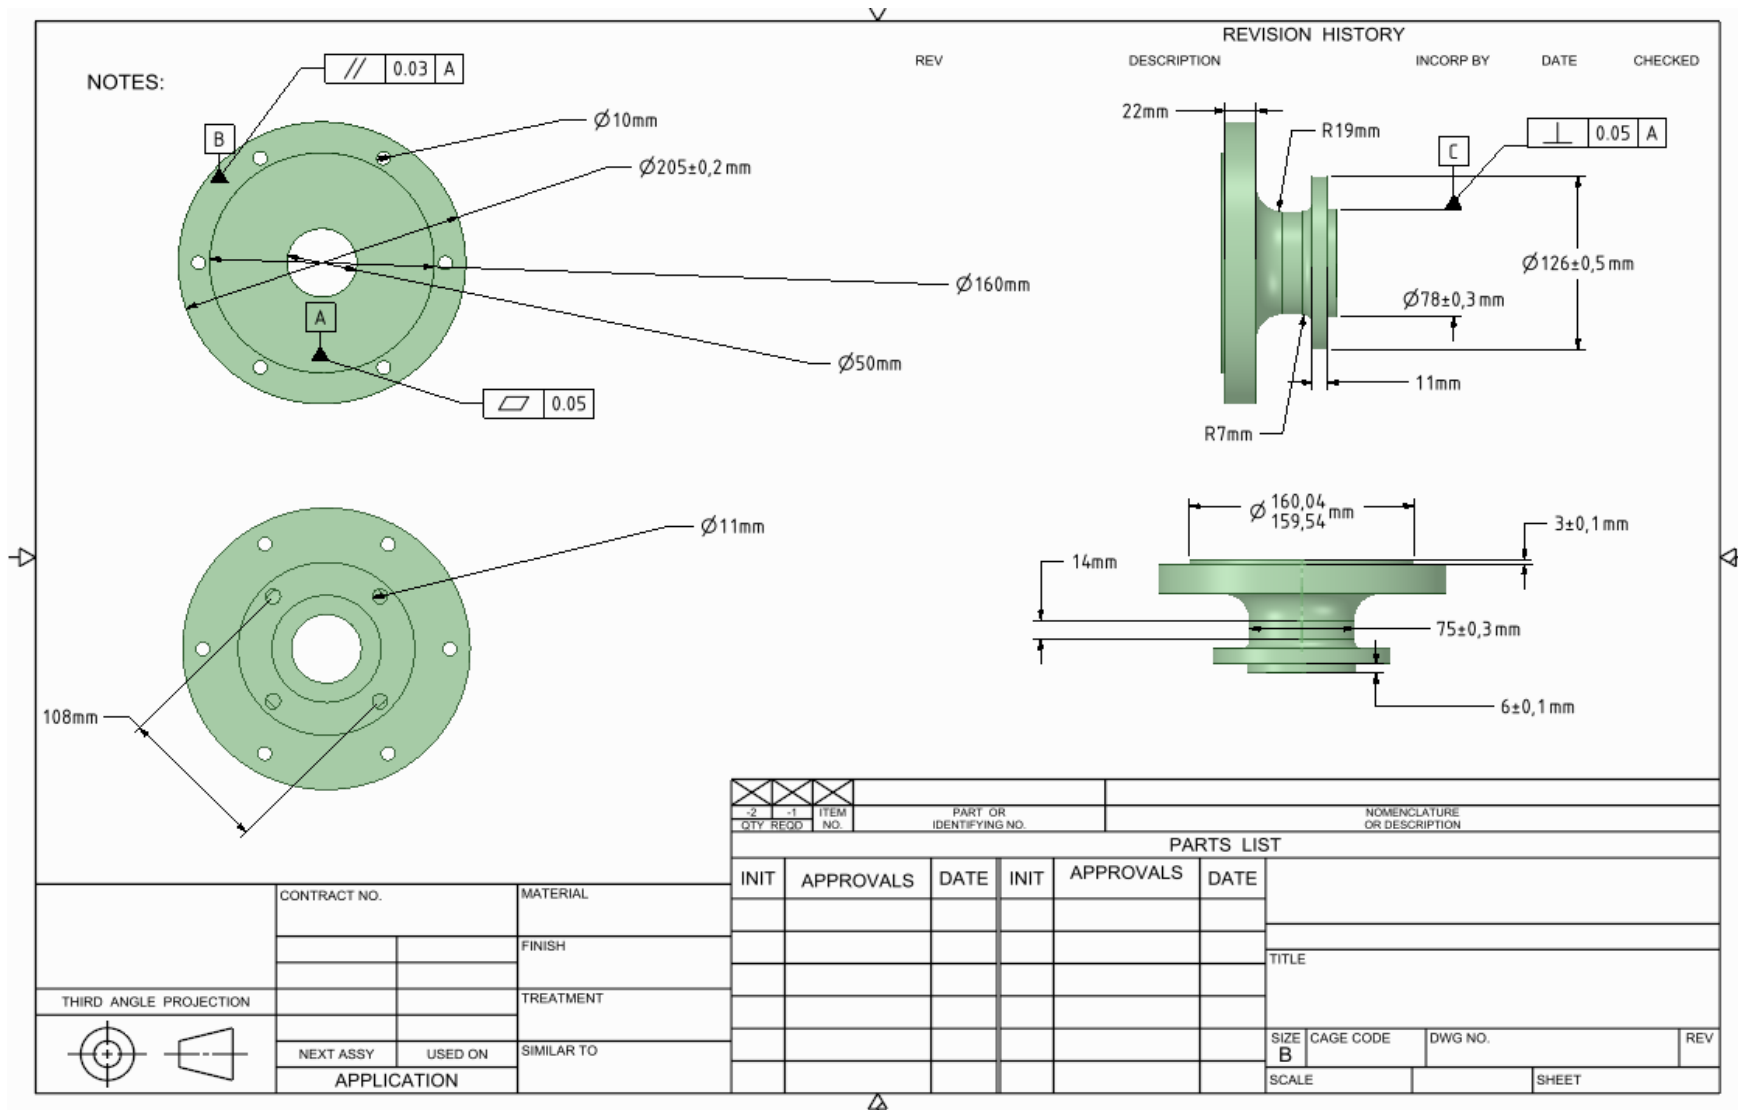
Plano de fabricación de elemento de conexión flange. Fuente: Elaboración propia.
